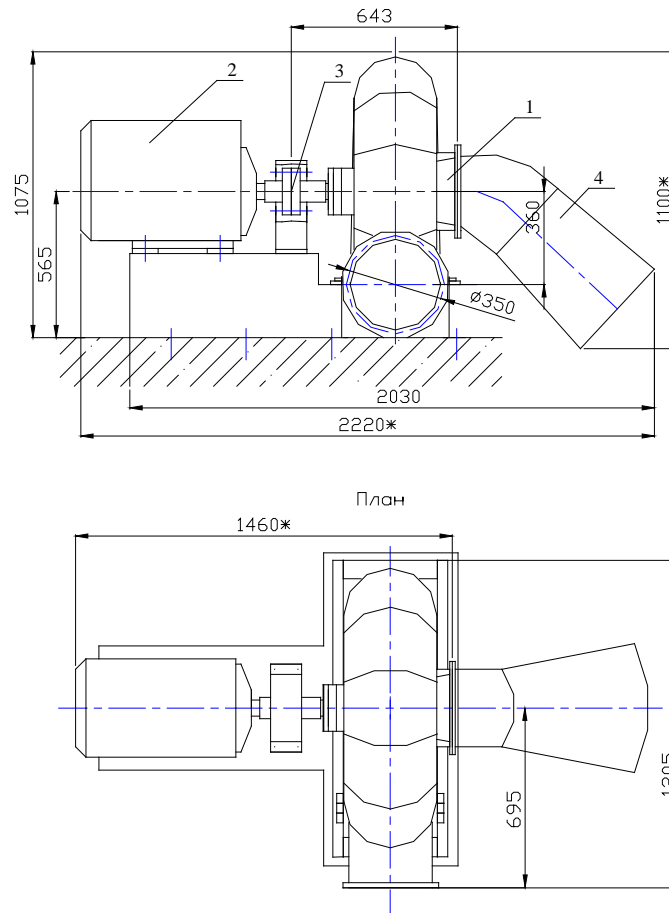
Габаритные и установочные размеры энергоблока с гидротурбиной ПрД55-Г20
